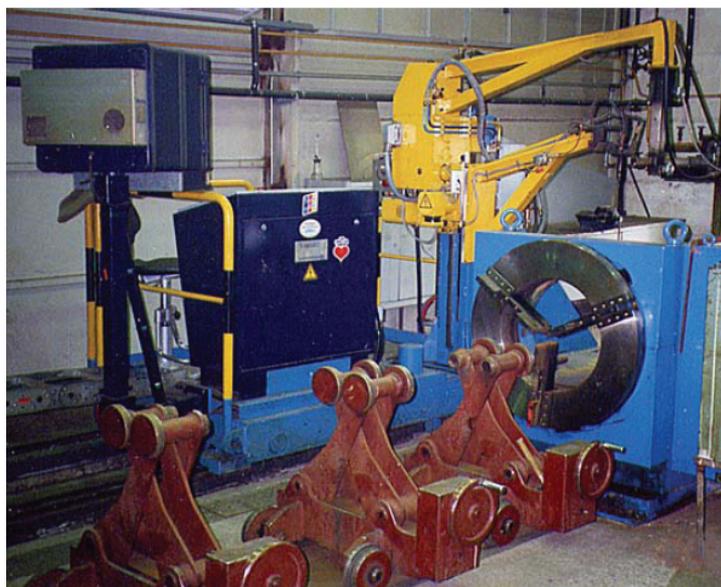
Комплекс с поворотным патроном для сварки труб
